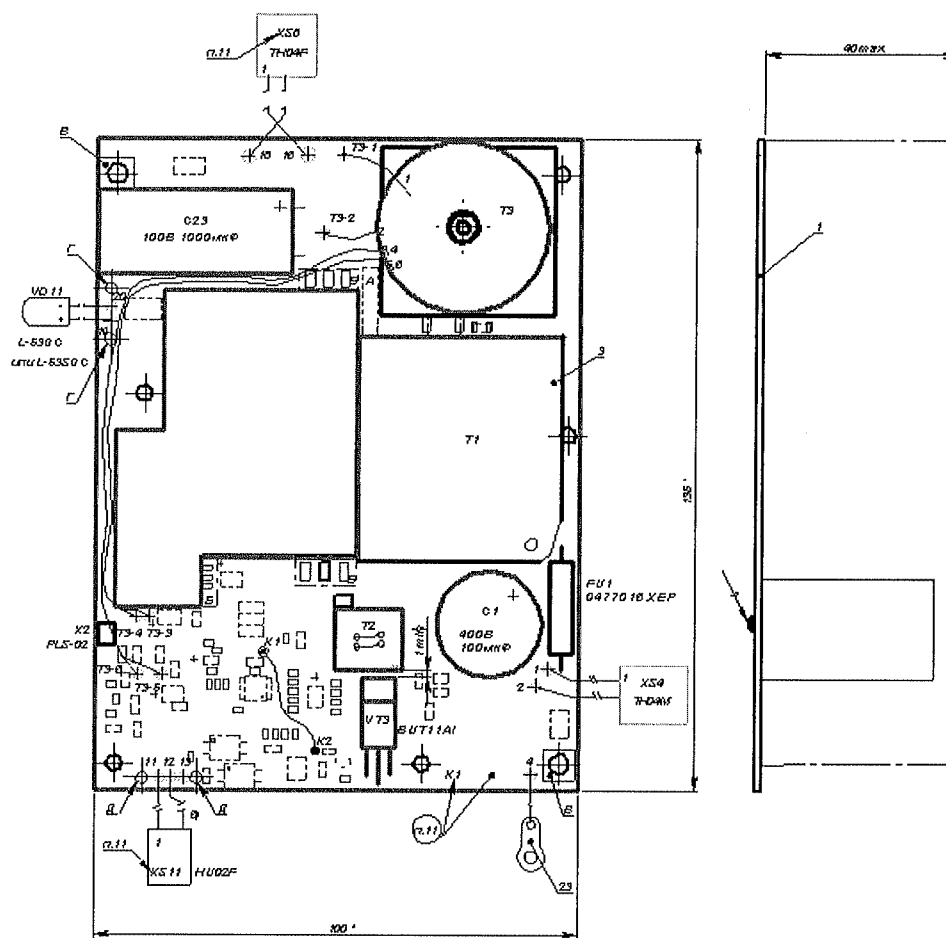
Сборочный чертеж платы преобразователя АГБР.240.85.20.00
